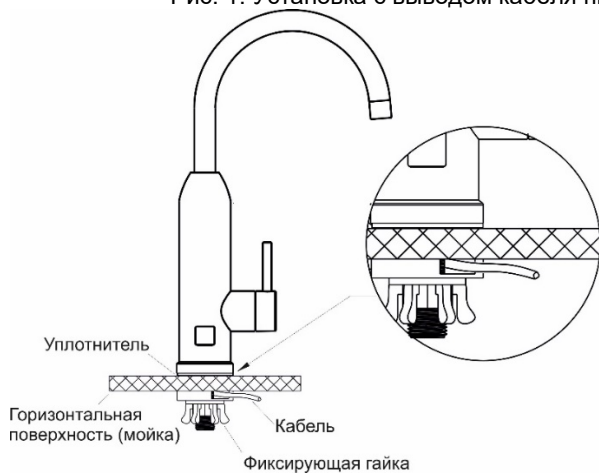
Установка с выводом кабеля питания под мойкой (схема крана ориентировочная).
